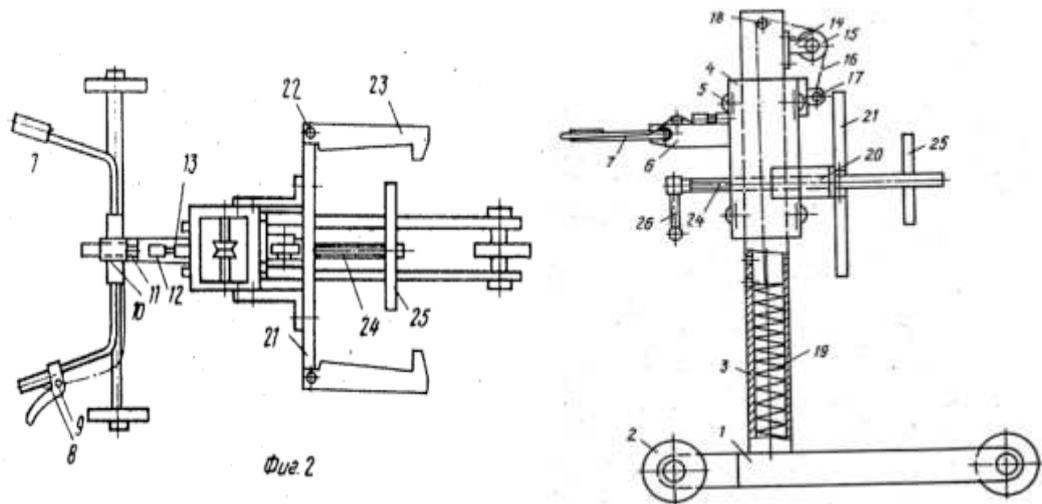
Устройство для демонтажа агрегатов транспортного средства.
